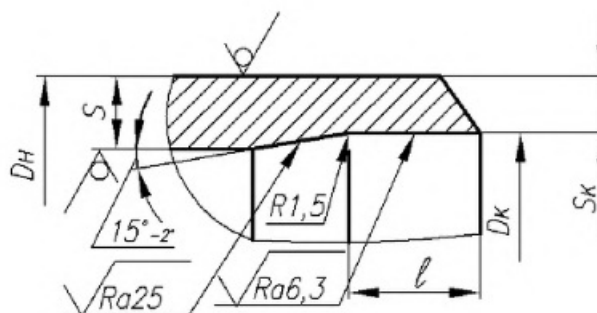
Цилиндрическая расточка труб для сварного соединения, подлежащего УЗК
